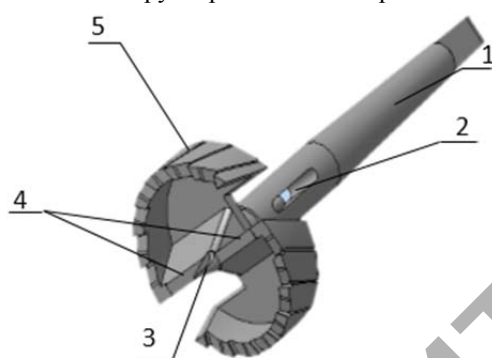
Модель инструмента: 1 — хвостовик (конус Морзе); 2 — паз для извлечения центрирующего элемента; 3 — центрирующий элемент; 4 — главные торцевые лезвия; 5 — цилиндрическая направляющая поверхность
